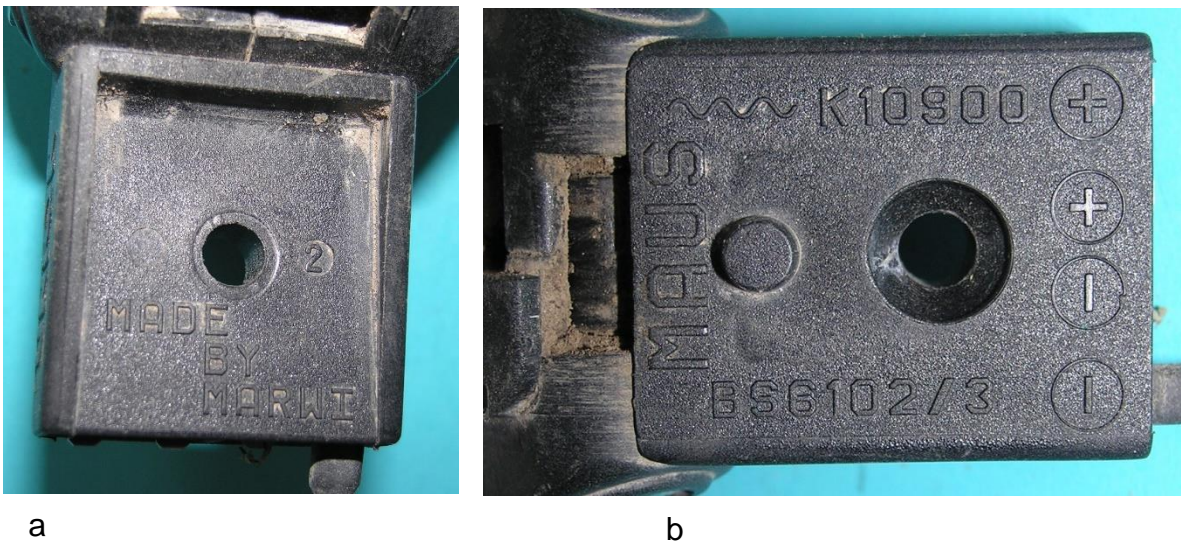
Beschriftungen des Kabelanschlusskastens: a) Made by Marwi, b) Oben: K 10900, senkrecht links: MAUS, unten: BS6102/3, senkrecht rechts: Polaritätskennzeichnung der Kabelanschlusstecker
